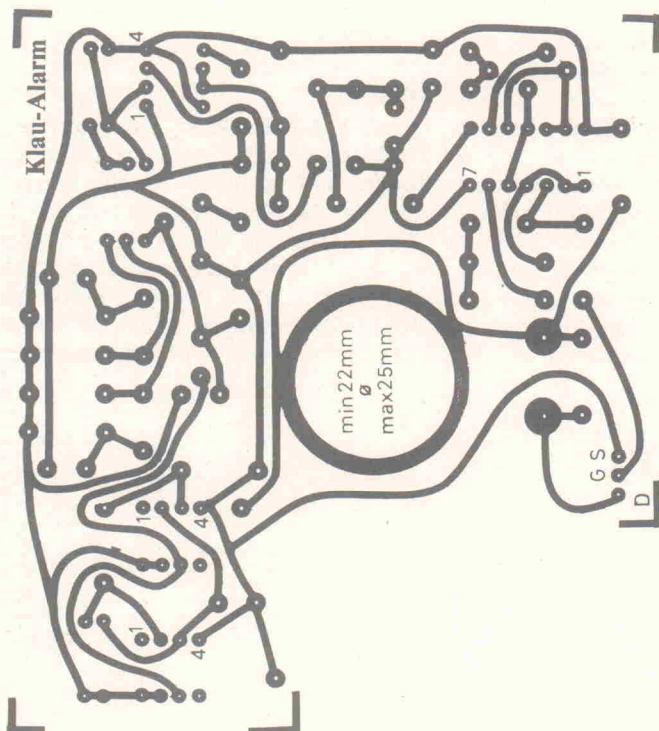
Das Platinen-Layout für die Fahrrad-Alarm-Schaltung.
